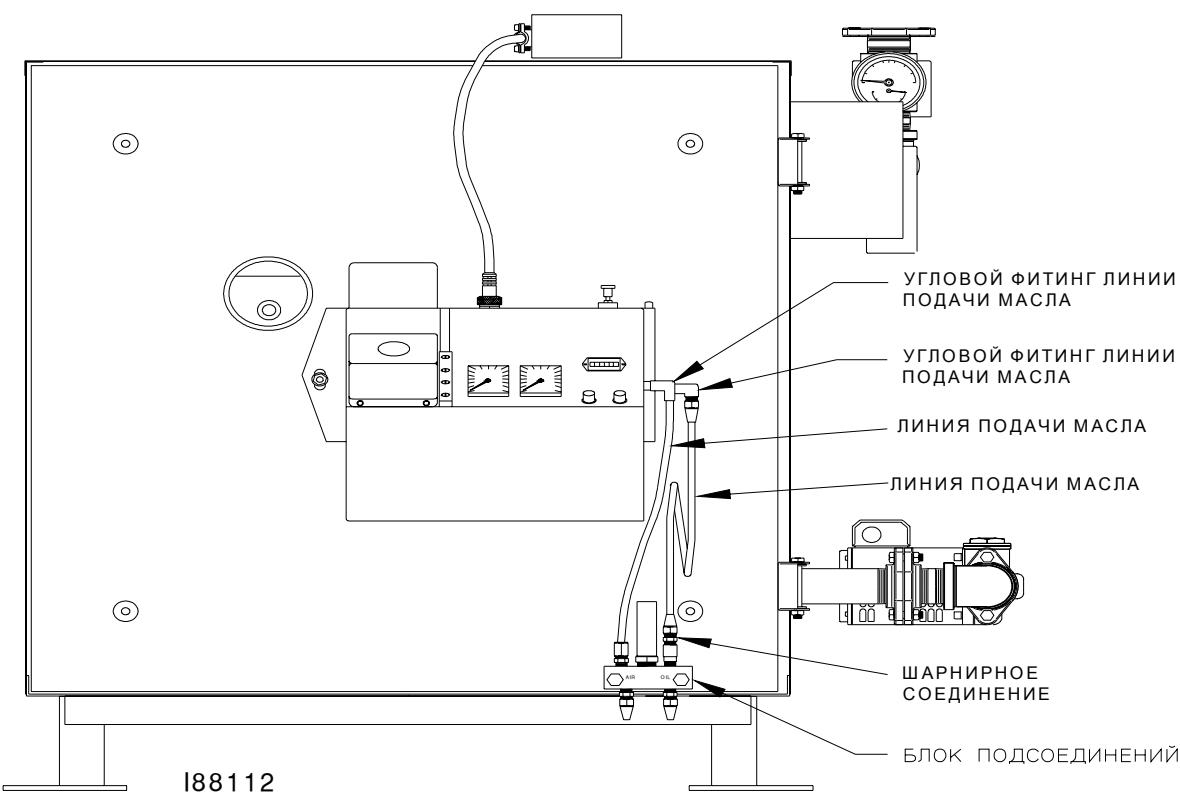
I – Установка блока подсоединений, воздуха (вид спереди)
